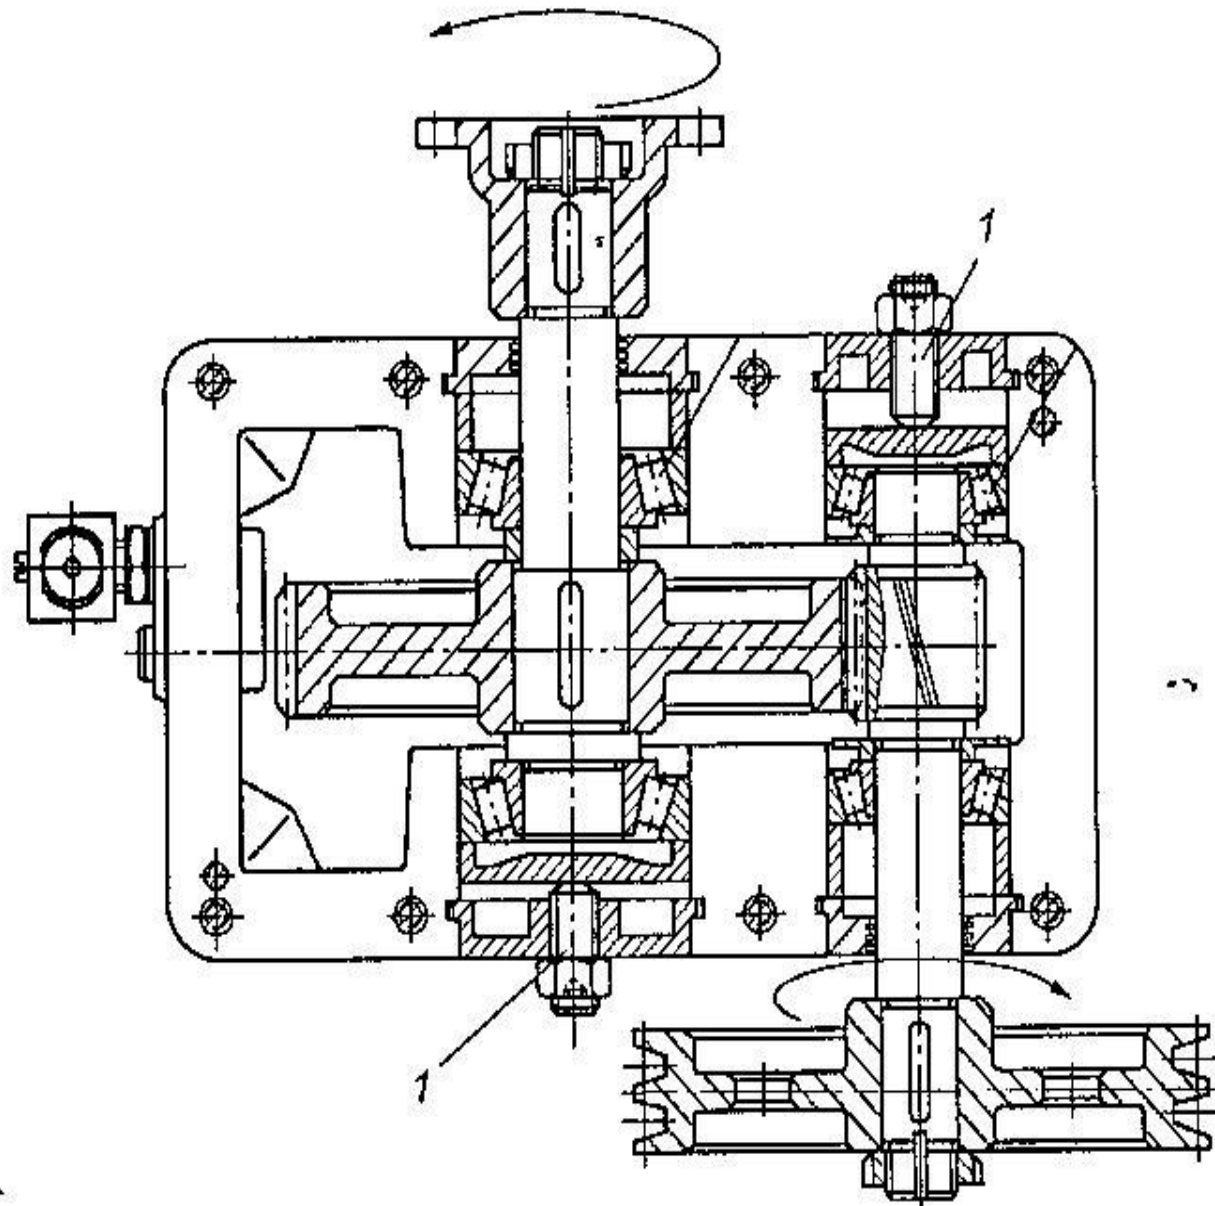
Цилиндрический одноступенчатый редуктор с горизонтальным расположением валов и их установкой на конических подшипниках враспор: 1 — винт
